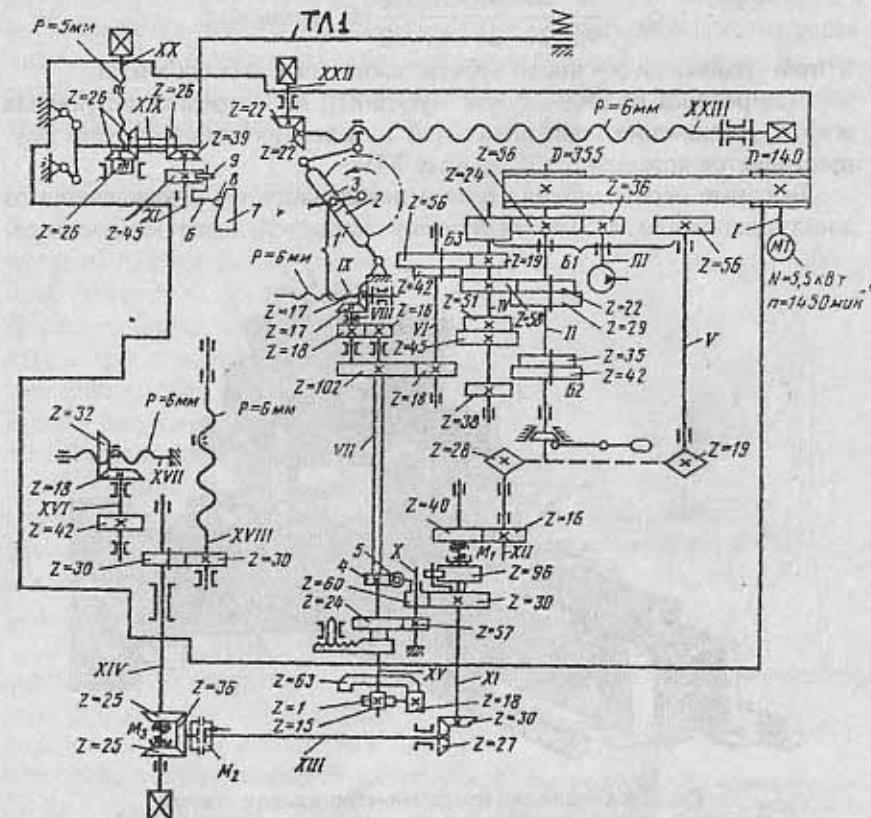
Кинематическая схема поперечно-строгального станка мод. 7Е35
